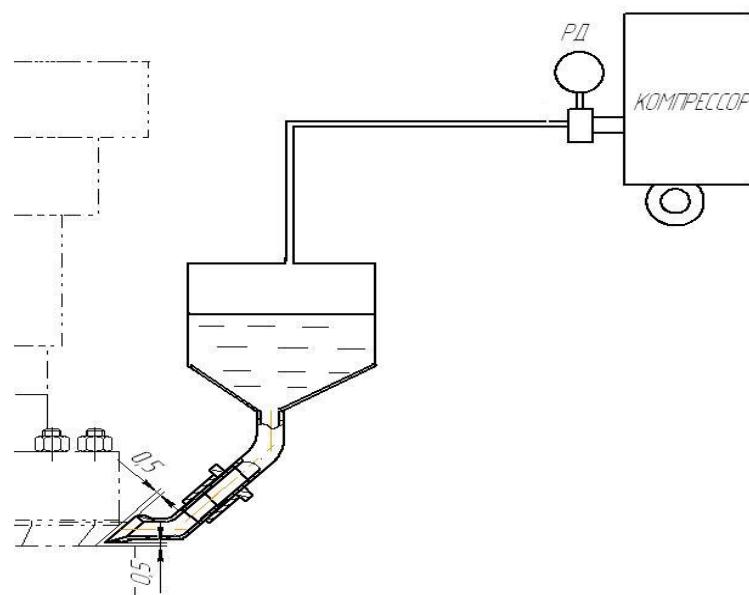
Схема нанесения консистентной смазки на зубья фрезы
